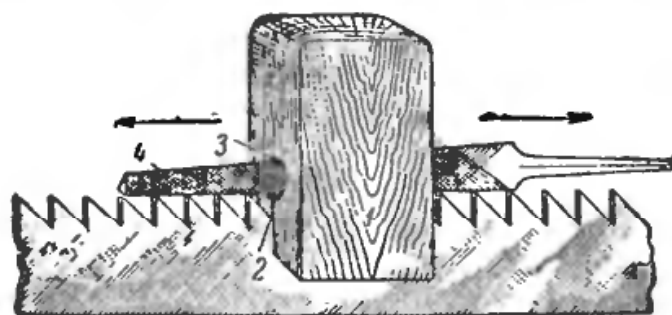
Прибор для выравнивания вершин зубьев после заточки пилы: 1—деревянный брусок для закрепления напильника; 2—прорезь для полотна пилы; 3—отверстие для напильника; 4—напильник.
